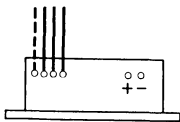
Drehstrommotor mit Schweißmaschine in einem Gehäuse.
